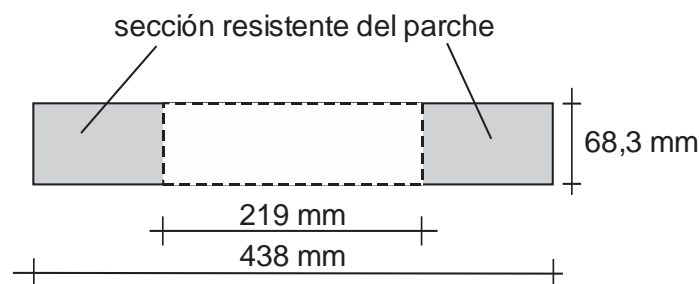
Sección transversal del aro de refuerzo (“parche”).
